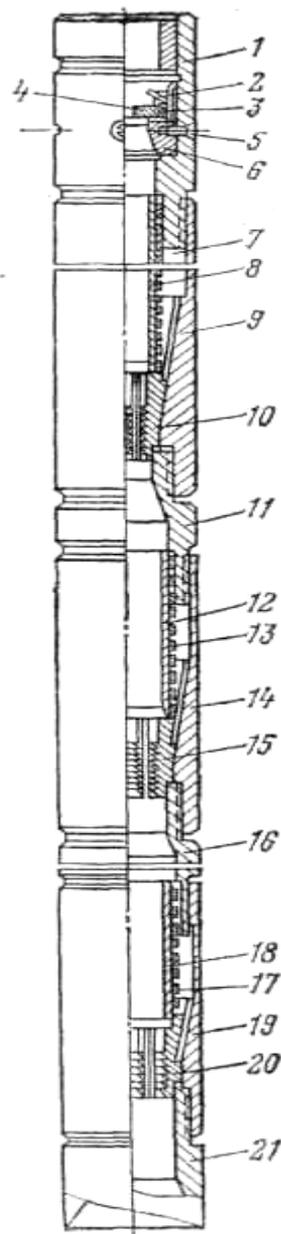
Комбинированный ловитель ЛКШТ:
